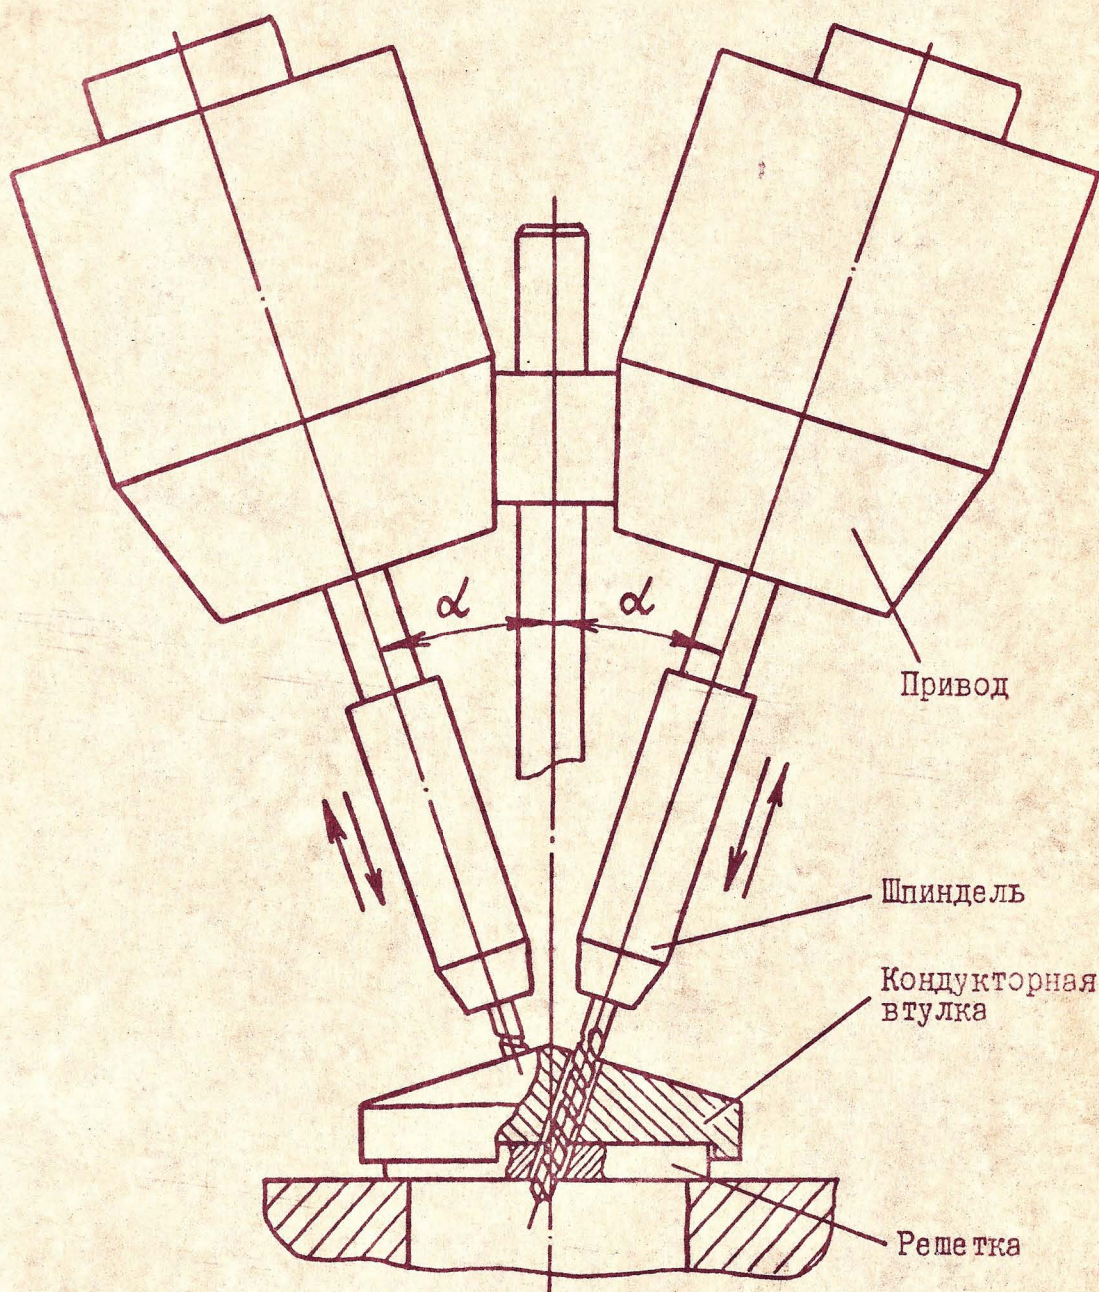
Схема установки шпинделей в сверлильном станке для изготовления решеток с наклонными отверстиями
